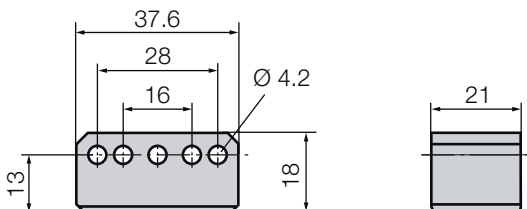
Dimensions de montage du capteur de position BTL6-A-3801-2
